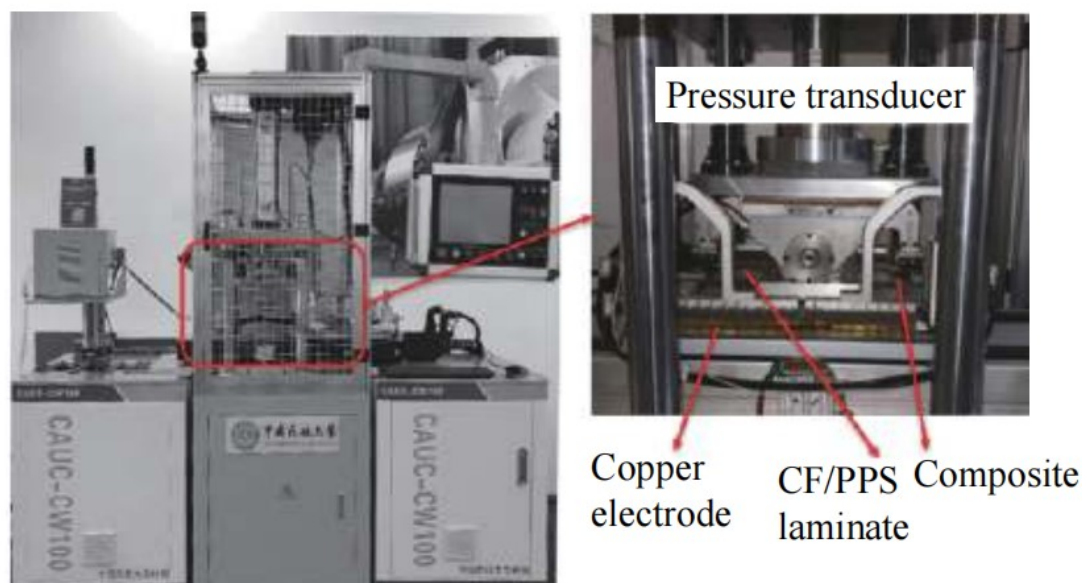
热塑性树脂基复合材料焊接设备
